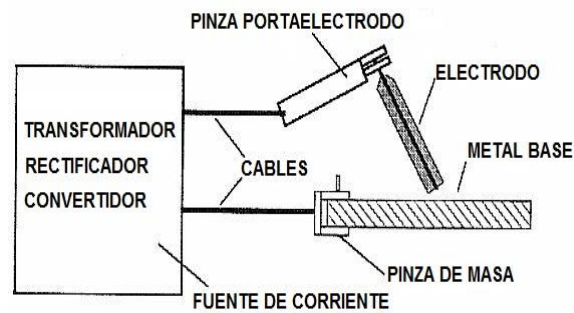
Esquema de los componentes proceso de soldadura SMAW.
